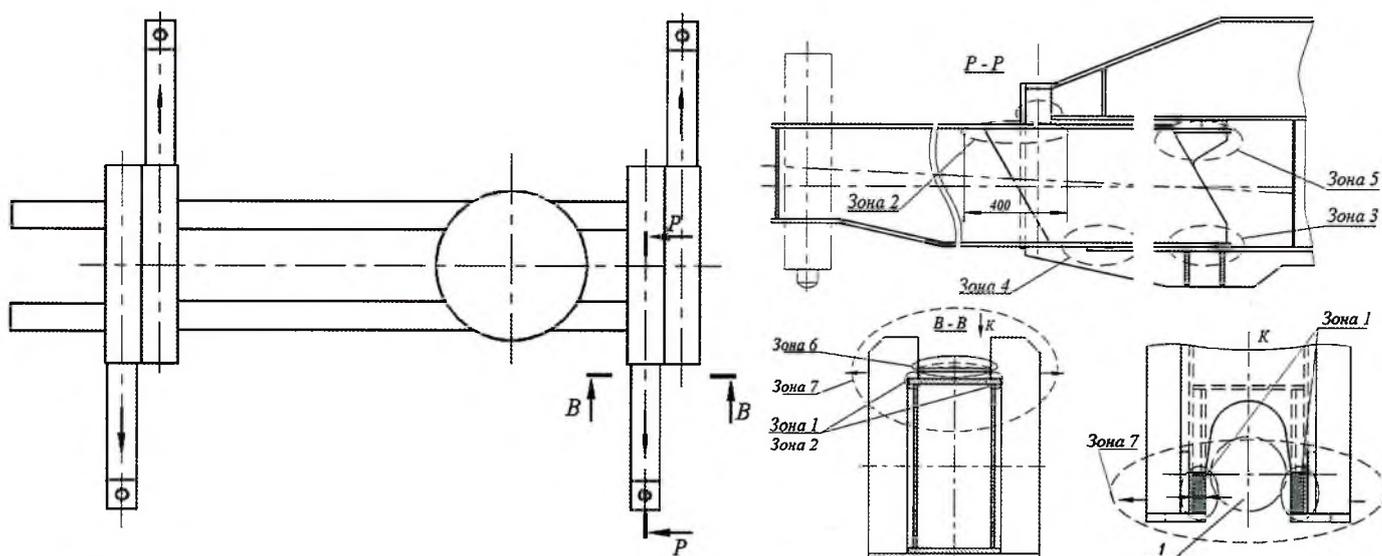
Схема опорной рамы, конструкции выносной опоры (P-P и B-B) и поперечной балки выносной опоры (K) кранов типа КС-6973
